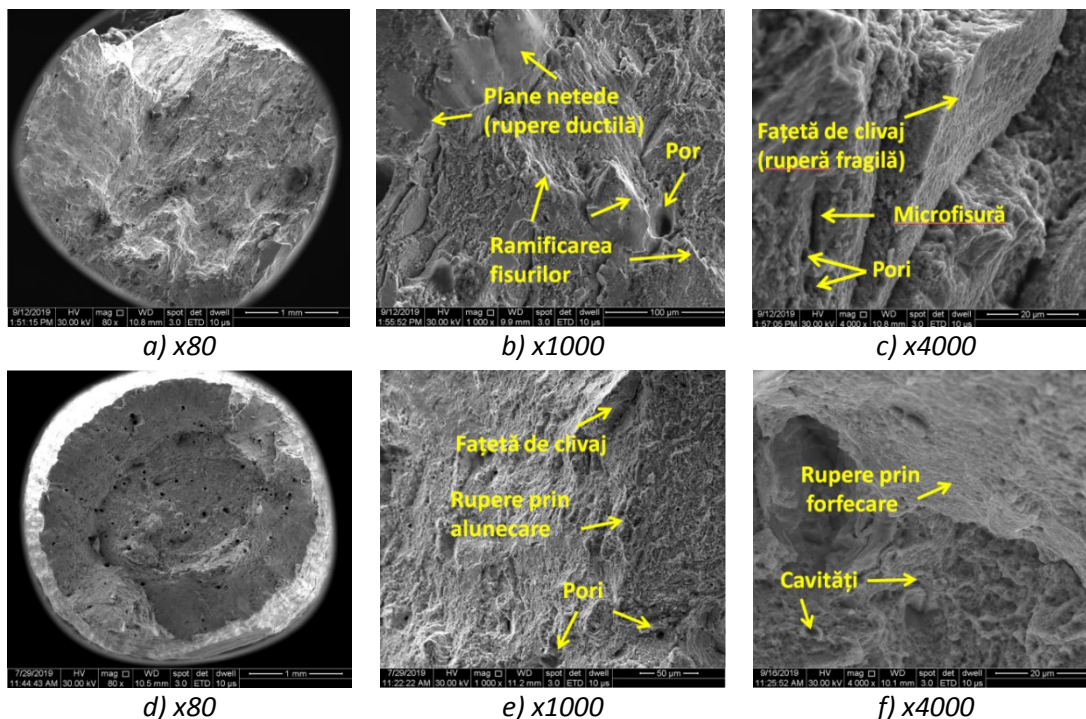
Suprafețele de rupere ale epruvete fabricate aditiv: (a-c) în plan orizontal și (d-f) în plan vertical
